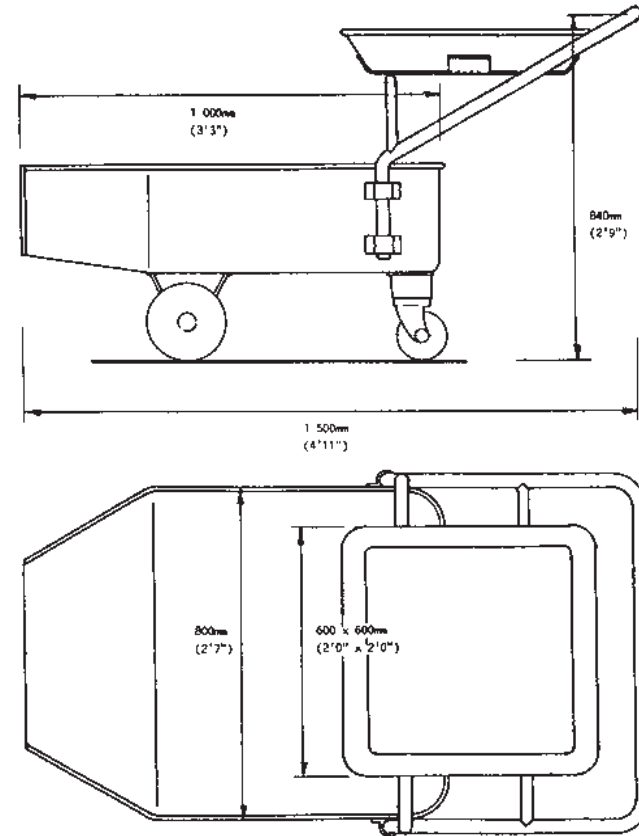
CARRETILLA PARA LA INSPECCION Y EL TRANSPORTE DE VISCERAS
